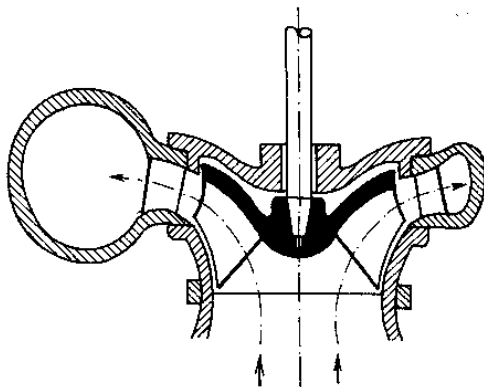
Bomba semi-axial ou de fluxo misto.
